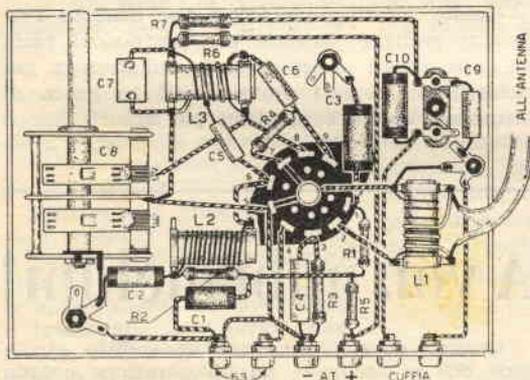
Il sistema di cablaggio di questo ricevitore è qui chiaramente rappresentato, assieme al modo di disporre le varie bobine.
